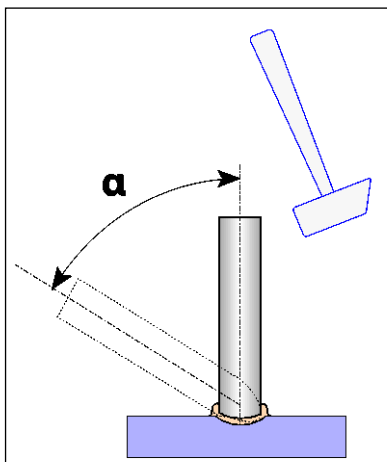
Sichtprüfung einer Bolzenschweißung
